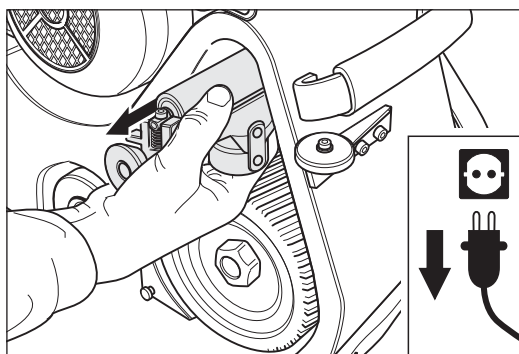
Das Aggregat vorsichtig aus dem Maschinengehäuse nehmen.
